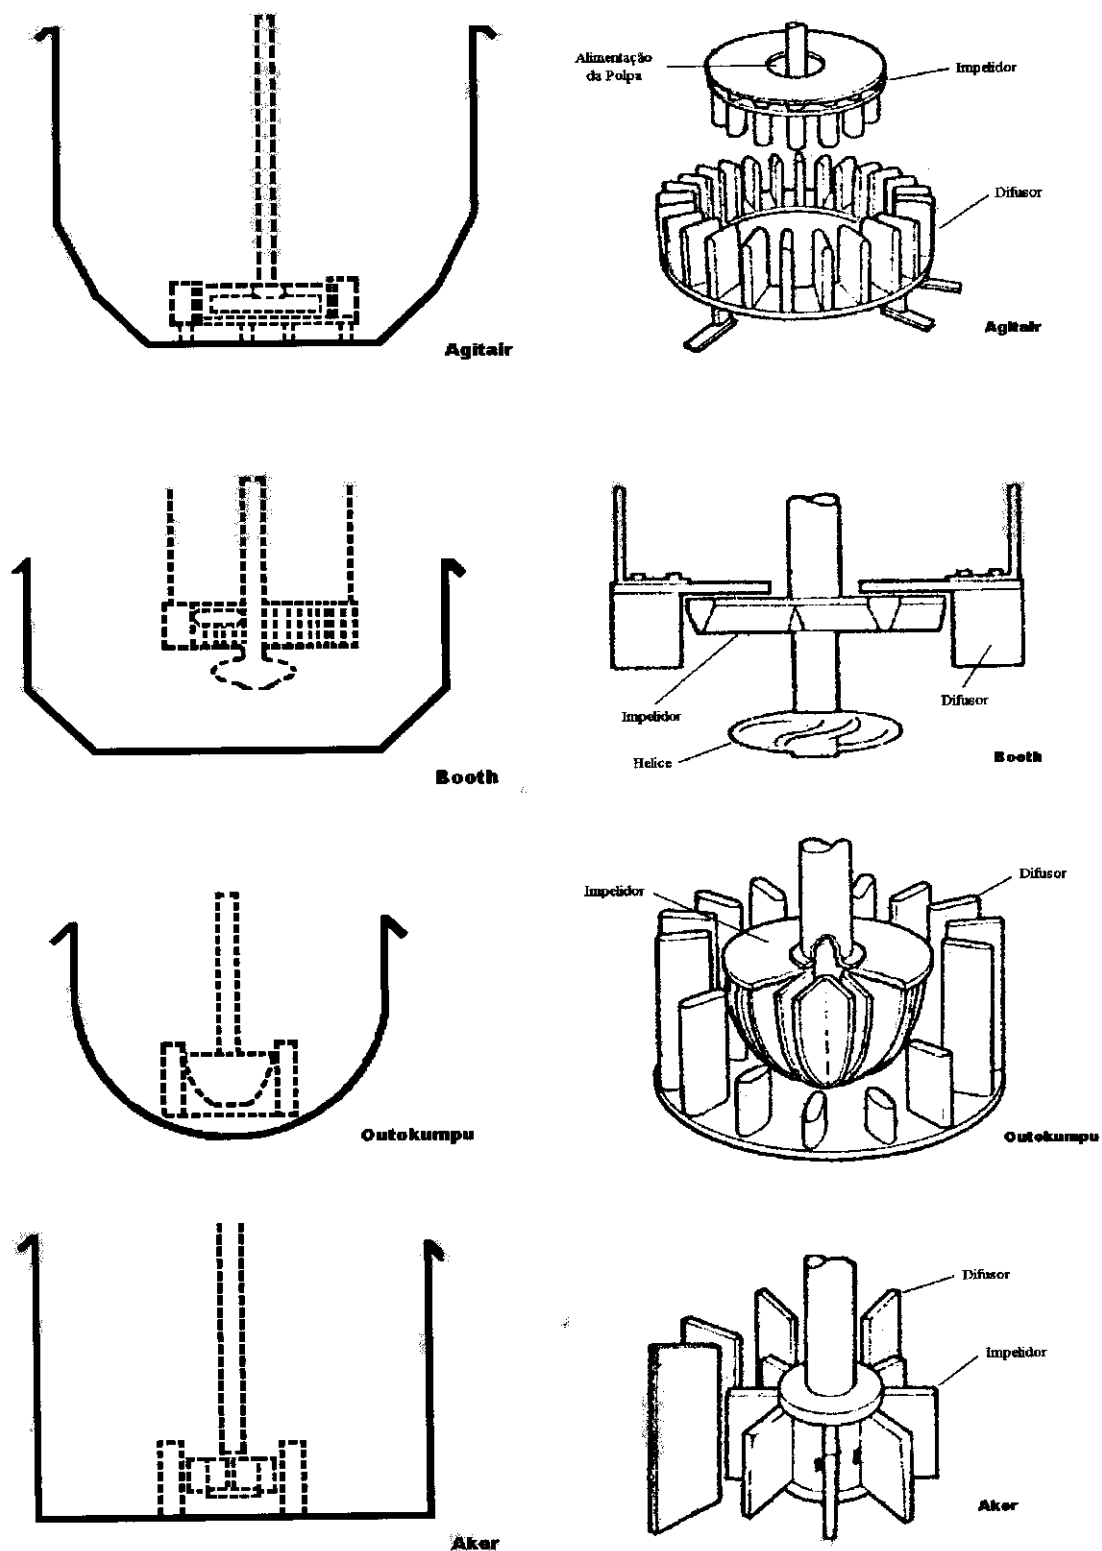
Desenho esquemático de tanques e rotores das células mecânicas Agitair, Booth, Outokumpu e Aker
